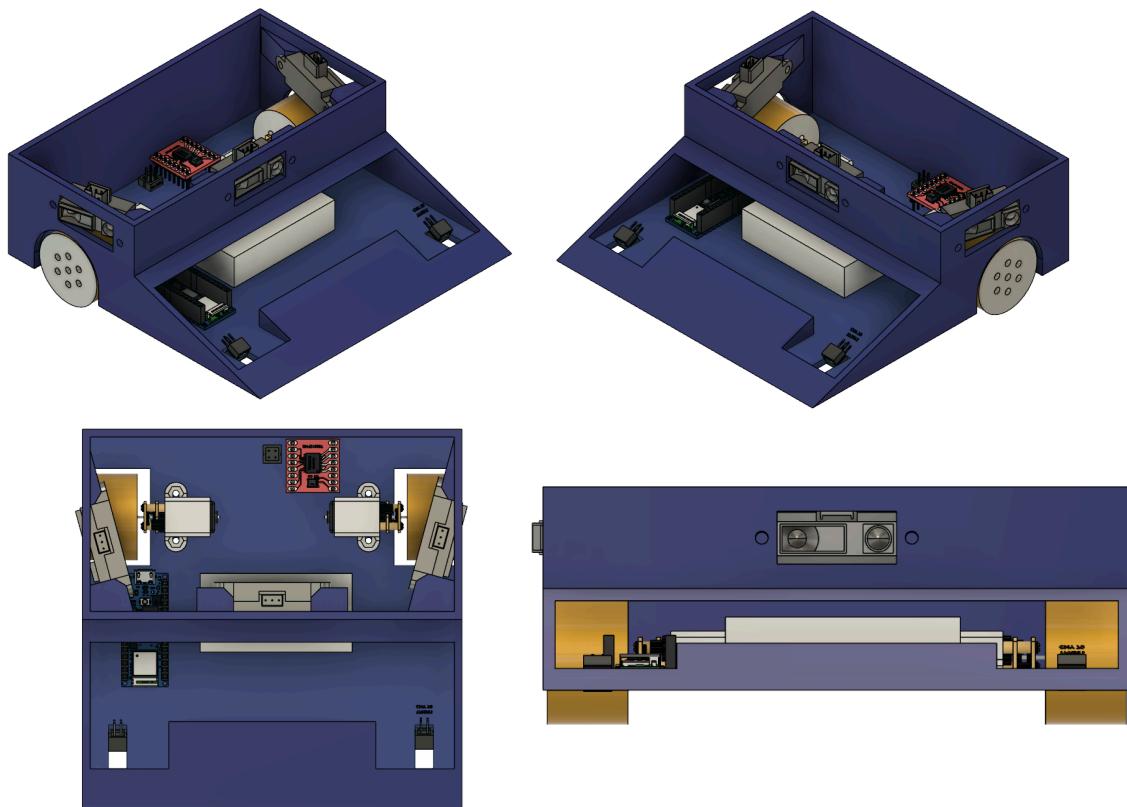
Diferentes vistas del chasis con la posición de los componentes en su interior.
